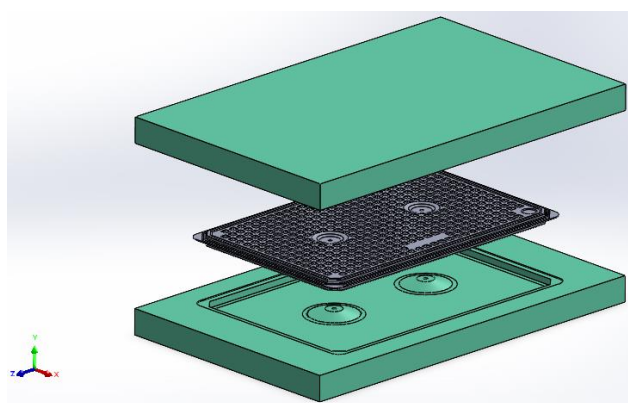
Vista explodida dos moldes de XPS e placa de alumínio de PCM (Solidworks).
